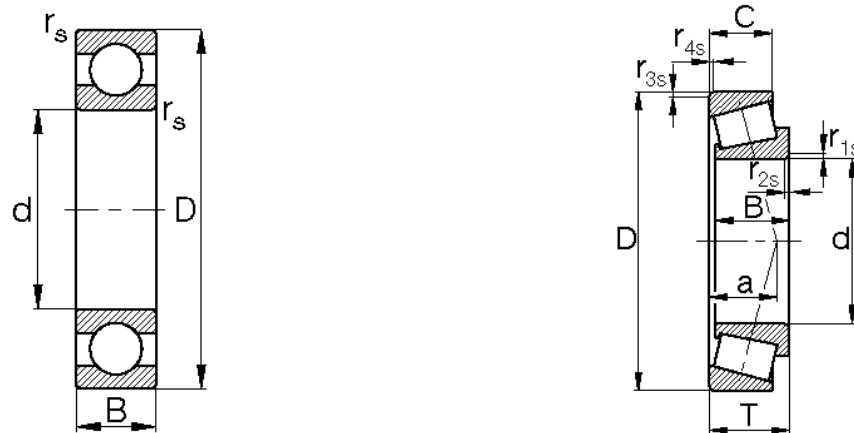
Dimensiones principales un rodamiento radial de bolas y de un rodamiento cónico.
